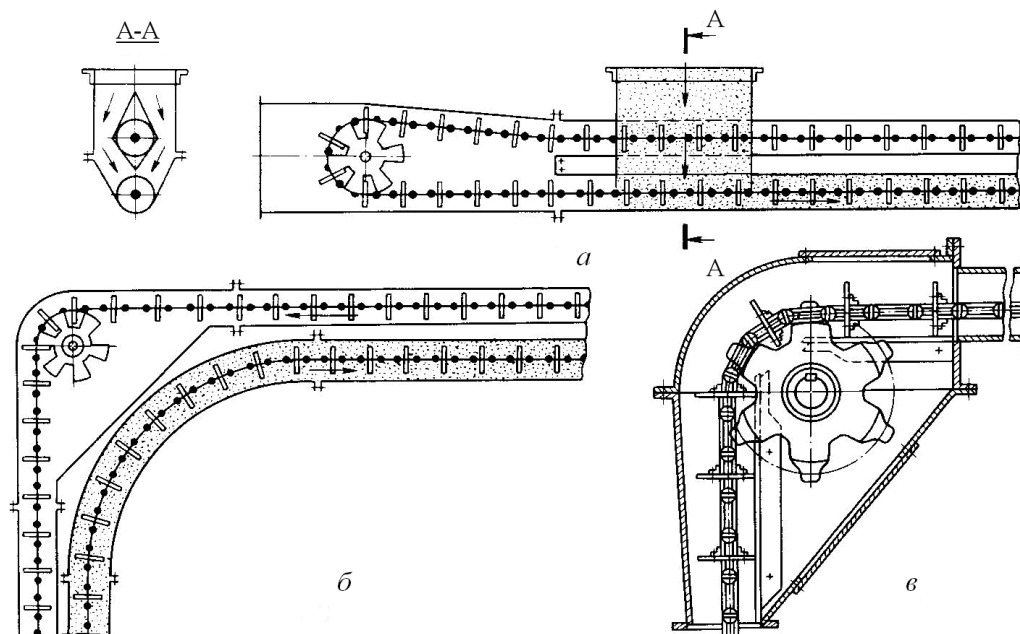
Схемы элементов трубчатых скребковых конвейеров:
